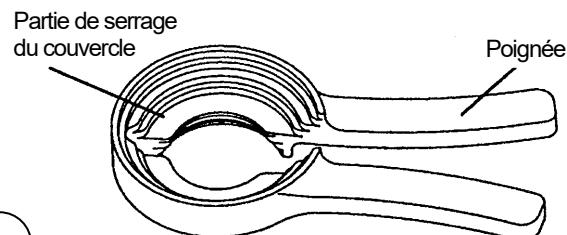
Vue extérieure de l'ouvre-couvercle 3
